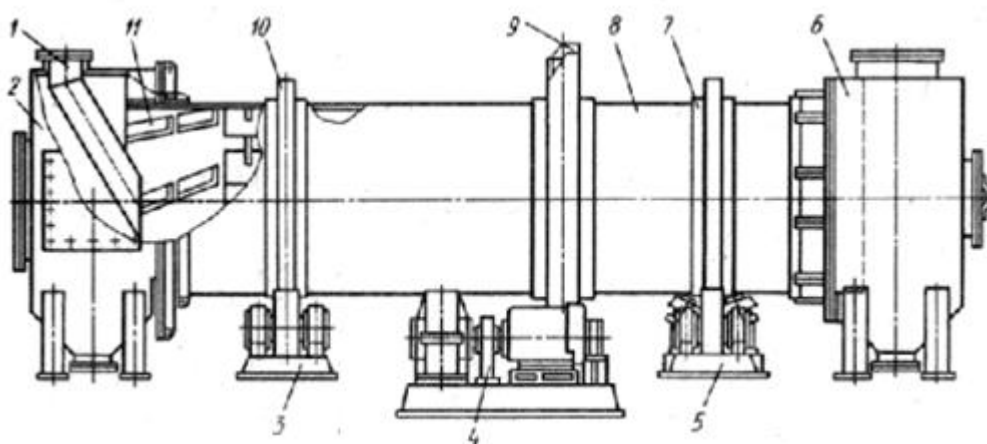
Зовнішній вигляд барабанної сушарки
